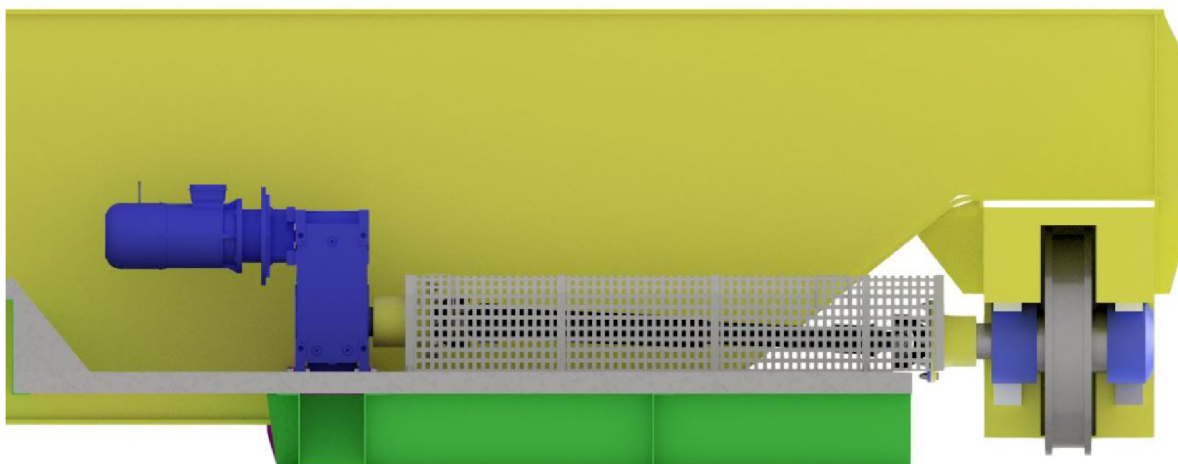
Mechanismy pojezdu – IZO pohled 2
